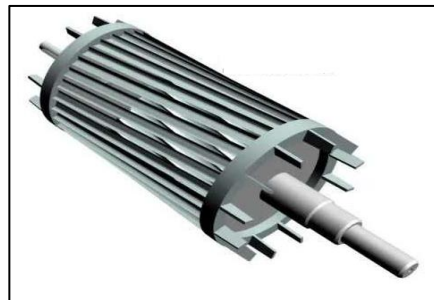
COMPONENTE DEL MOTOR – ROTOR
